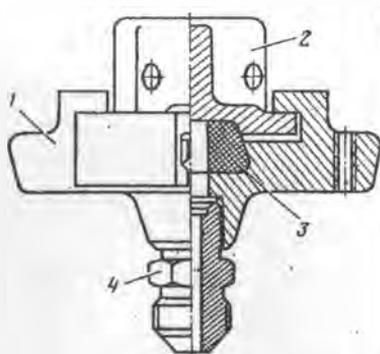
Бортовой зарядный штуцер 3509С50: 1 - корпус; 2 - крышка; 3 - резиновое кольцо; 4 - штуцер
